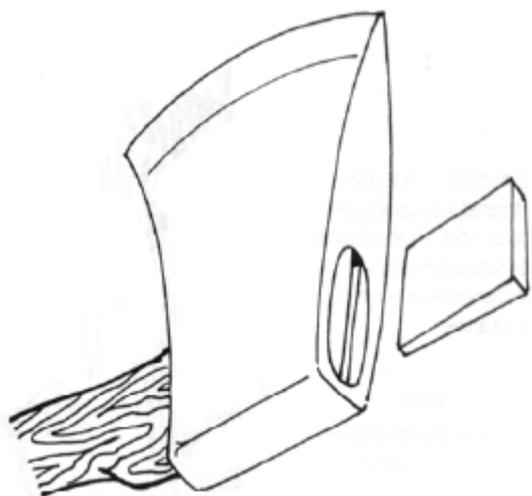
Detalhe da colocação da cunha de segurança da cabeça do machado
